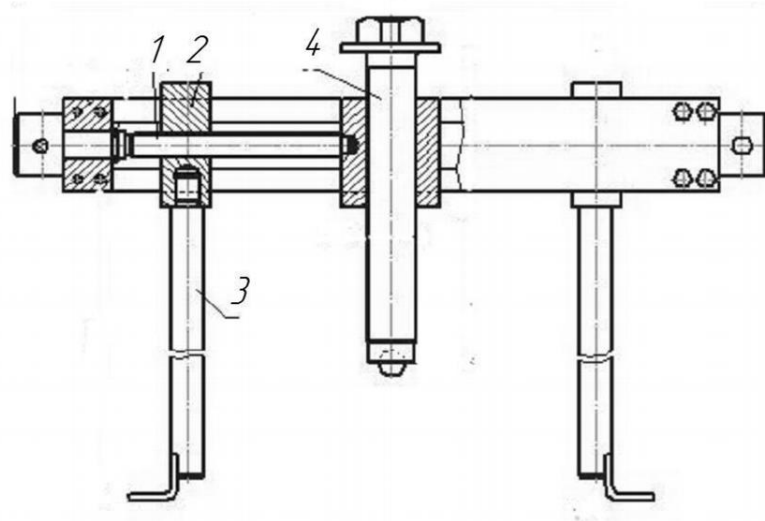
Знімач універсальний для випресовування підшипників із гнізд корпусів мод. Kraftool 1- 43310-130: 1 – Маточина-гайка; 2 – Регулювальний гвинт; 3 – Захват; 4 – Віджимний болт
